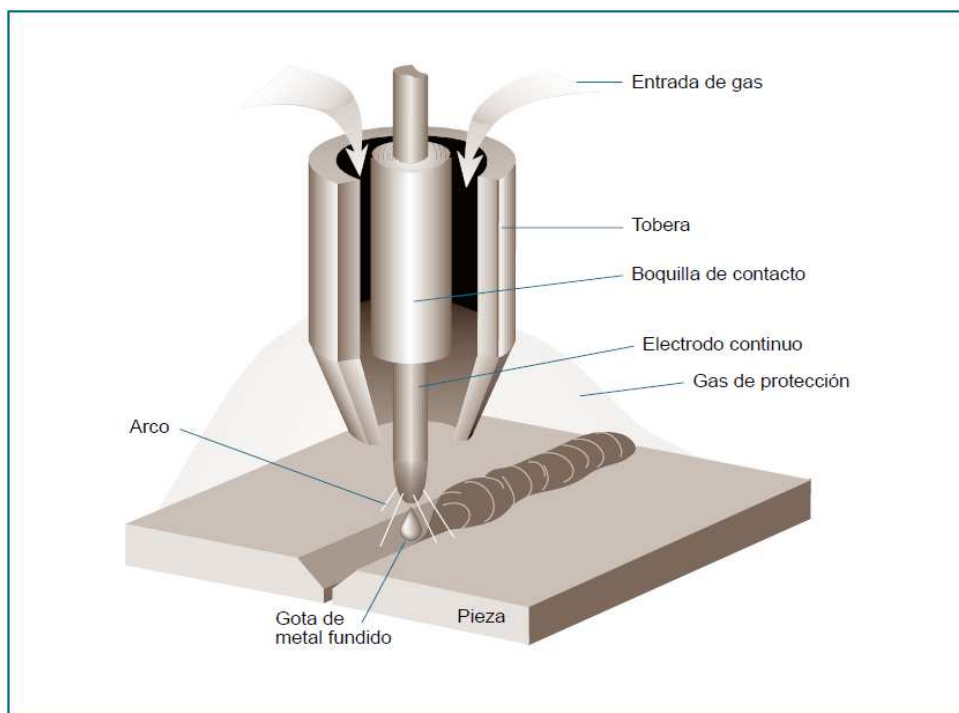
Fundamento del proceso de soldadura eléctrica al arco GMAW.
